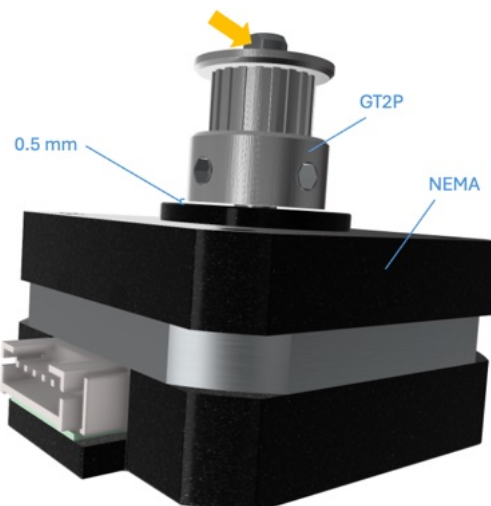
Rewinder-Chassis Montageschritt 4.
